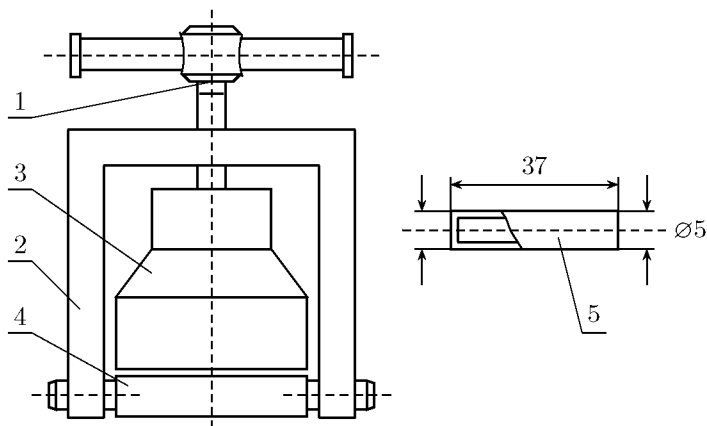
Прессформа для изготовления шаров из пластилина к исследованию абсолютно неупругого удара. 1 — выжимной винт; 2 — корпус прессформы; 3 — верхняя полусфера; 4 — нижняя полусфера; 5 — втулка резьбовая.
